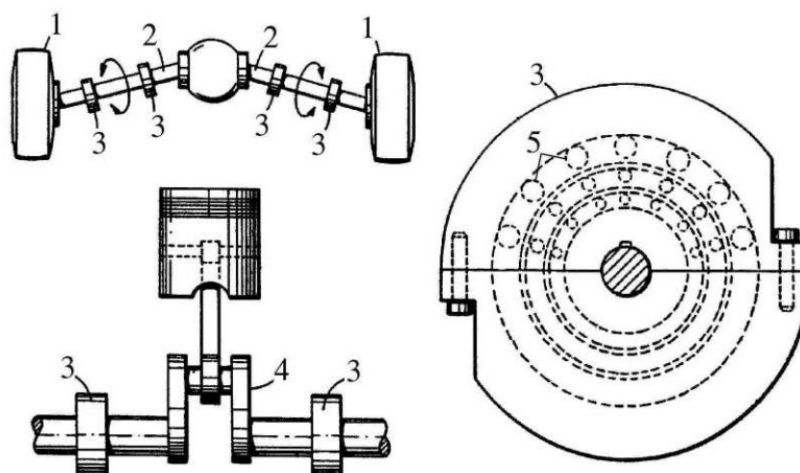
Patent US 5,460,017 Уравновешивания вращающихся частей автомобильных колес и коленчатого вала двигателя внутреннего сгорания: 1 - колесо, 2 - вал колеса, 3 - шаровой АБУ, 4 - коленвал, 5 – шары.
